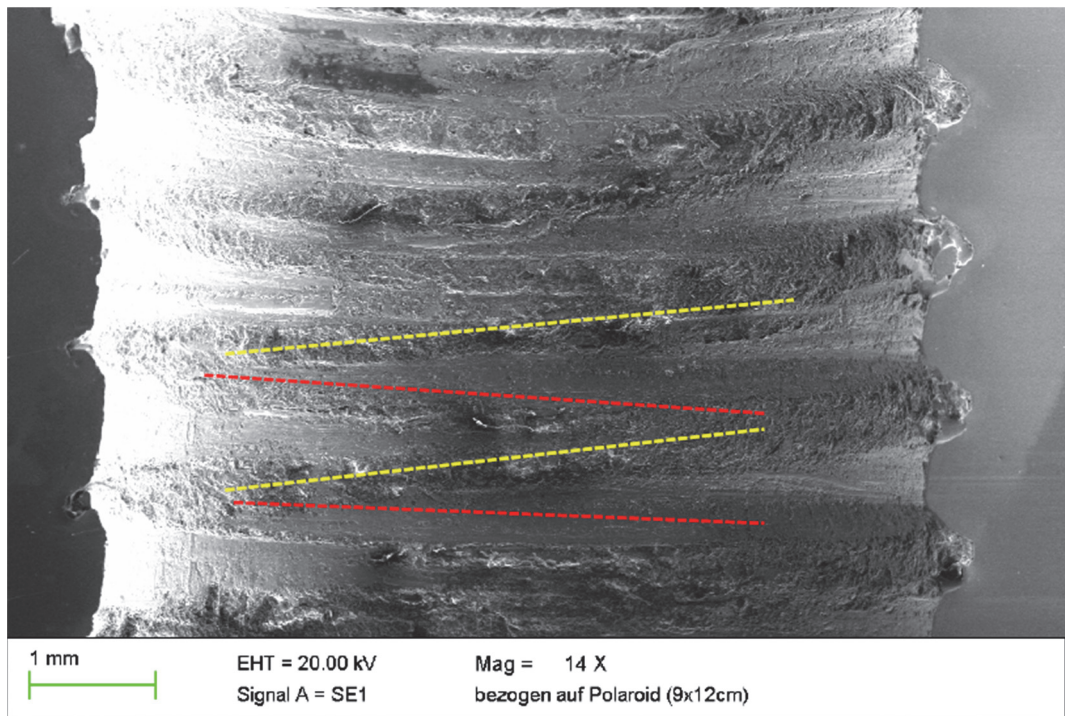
Innenaufnahme der Mutter vor dem Reinigen (aufgeschnitten). Es sind zwei verschiedene Gewinderichtungen (Rechts- und Linksgewinde) vorhanden.
